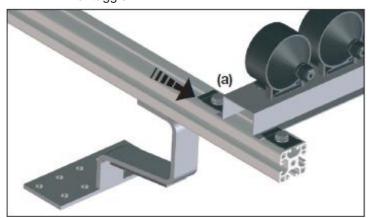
spingere la placchetta di serraggio (a) verso l'alto
